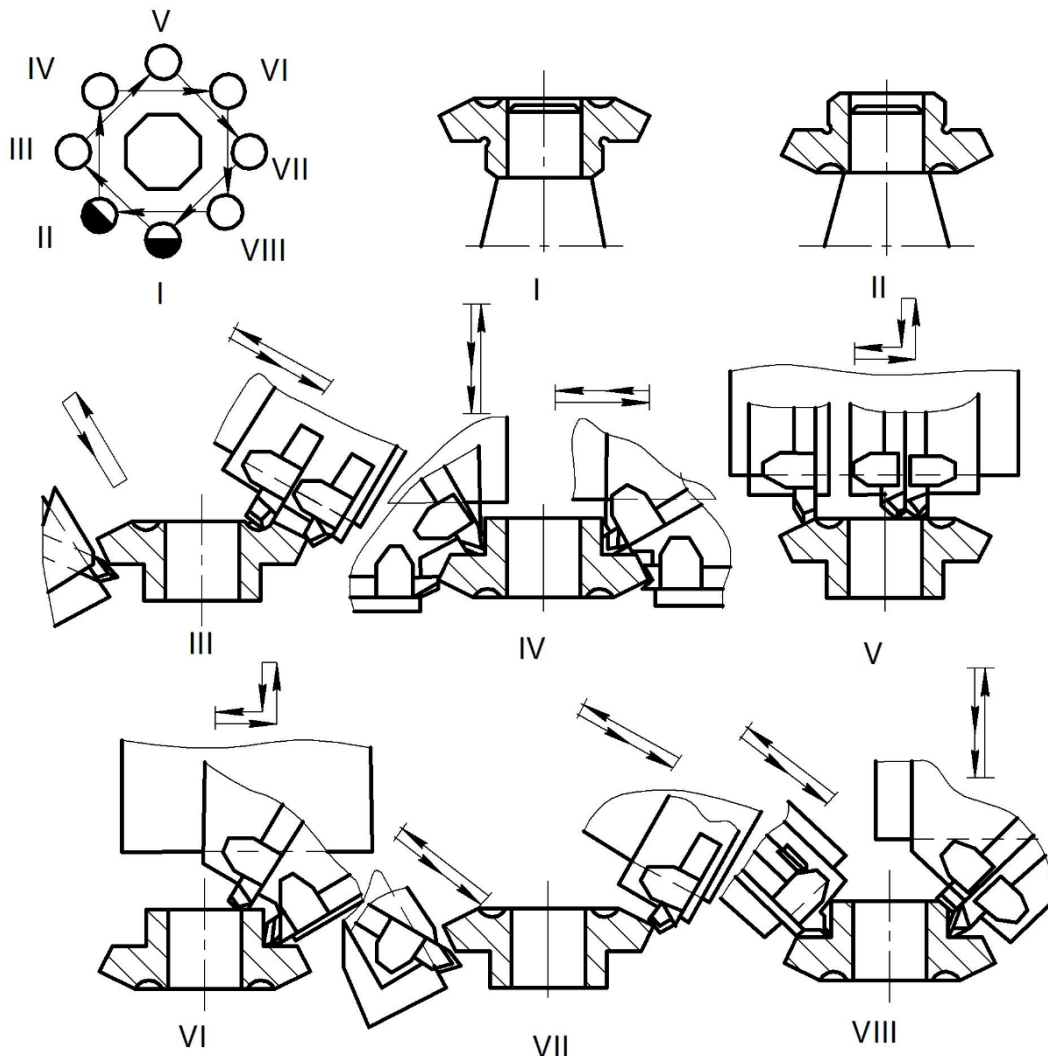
Технологічна схема налагодження 8-шпindelного токарного напівавтомата для оброблення заготовки зубчастого колеса-втулки за два цикли
